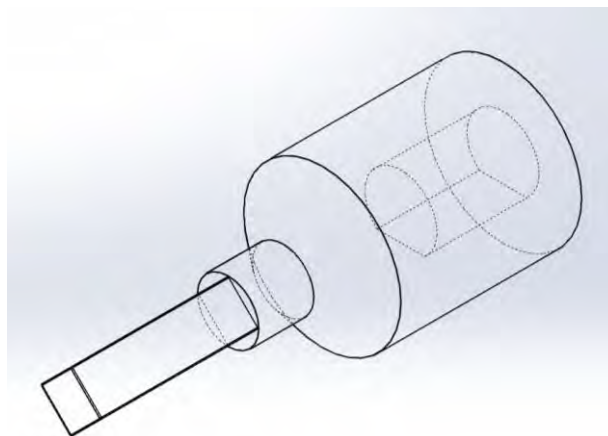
Diseño definitivo del adaptador motor – dispensador.
